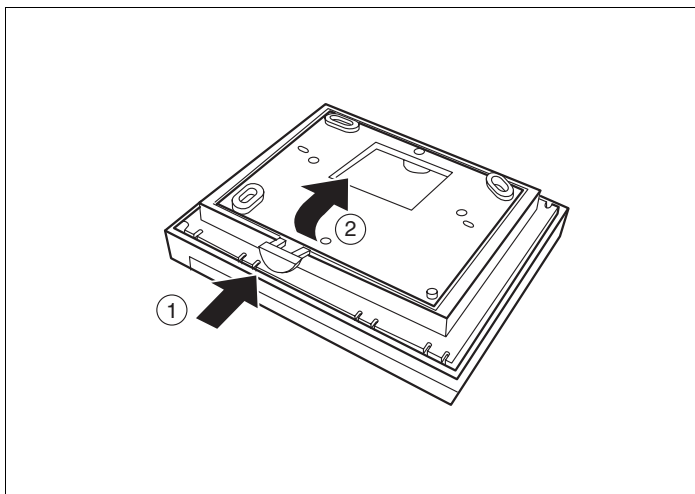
Se separa termostatul de încăpere de placa de montaj
